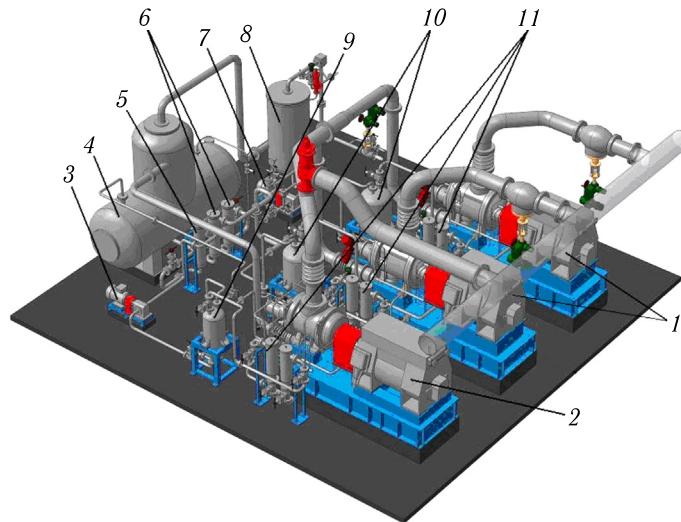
Общий вид гелиевого винтового компрессорного агрегата «Каскад-110/30»: 1 — два винтовых компрессора первой ступени сжатия; 2 — винтовой компрессор второй ступени сжатия; 3 — масляный насос; 4 — маслобак; 5 — фильтры грубой очистки второй ступени; 6 — фильтры грубой очистки первой ступени; 7 — пусковой масляный насос компрессоров первой ступени; 8 — сепаратор; 9 — маслоохладитель второй ступени; 10 — два маслоохладителя первой ступени; 11 — фильтры тонкой очистки
